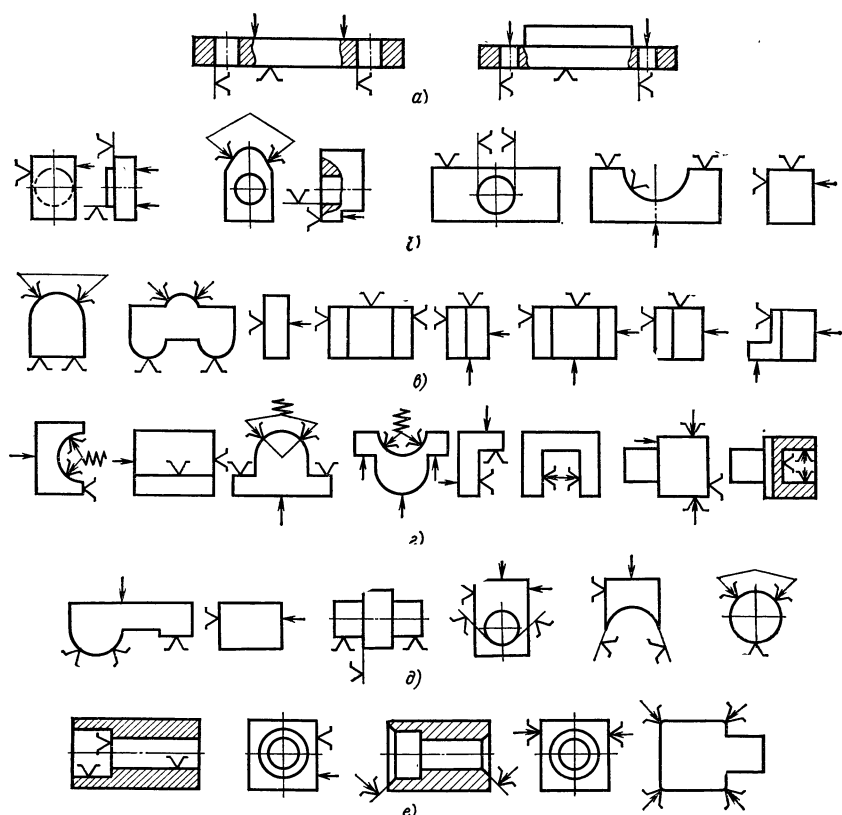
Схемы установки обрабатываемых деталей в приспособлениях АС и АЛ
